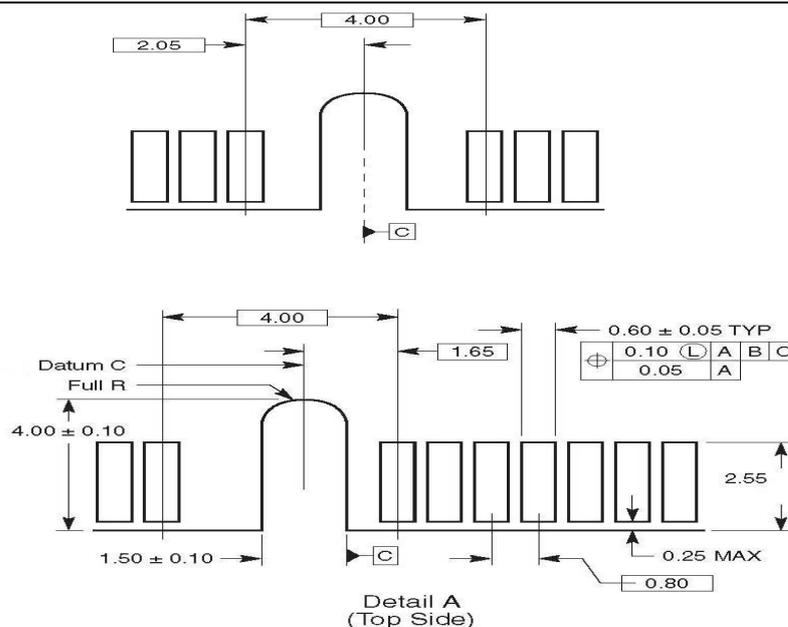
金手指 TOP 和 BOTTOM AB 处细节尺寸
